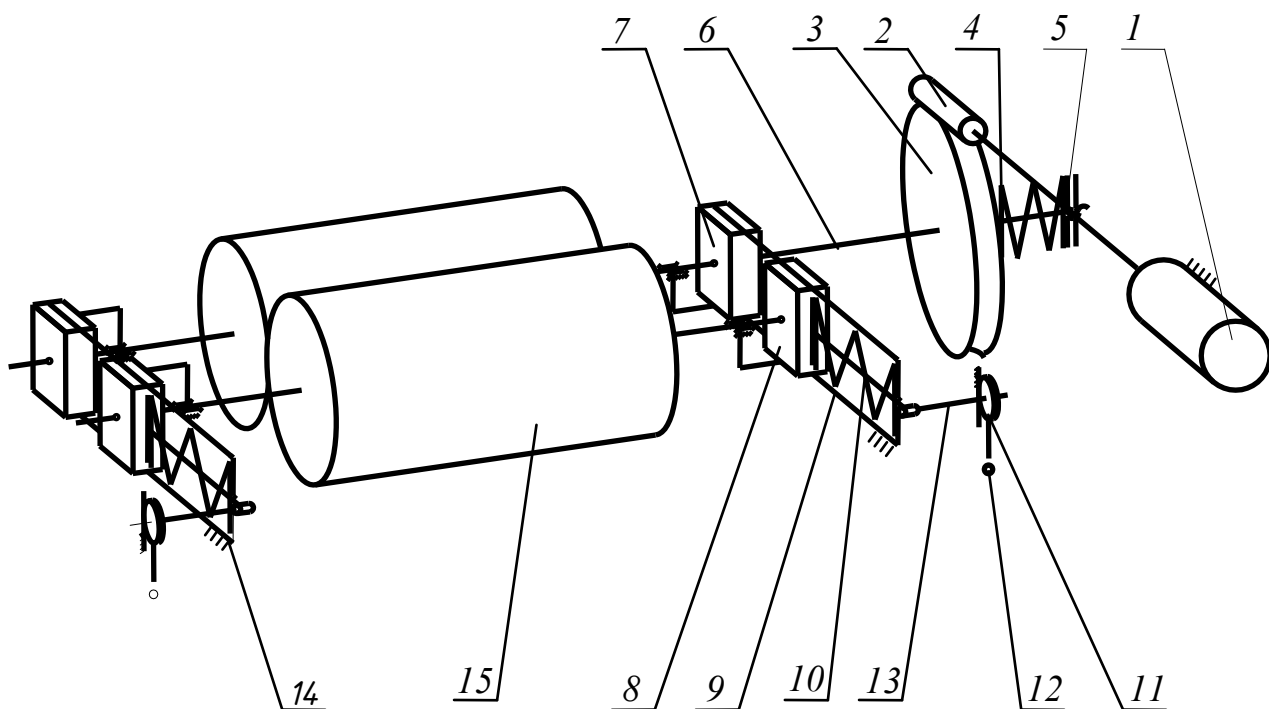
Кінематична схема механізму товаровідтягування
